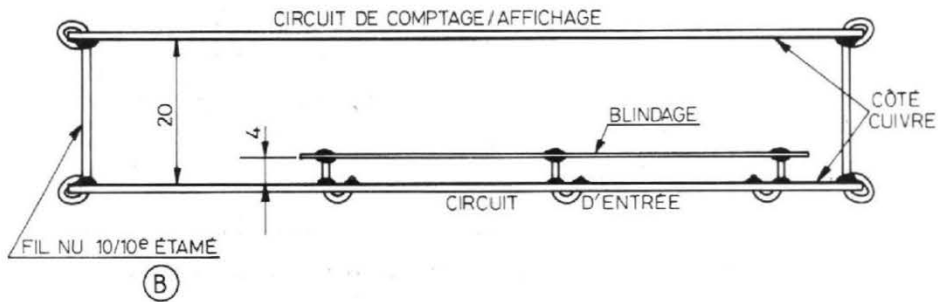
Montage mécanique de l'appareil et dessins du panneau avant.
